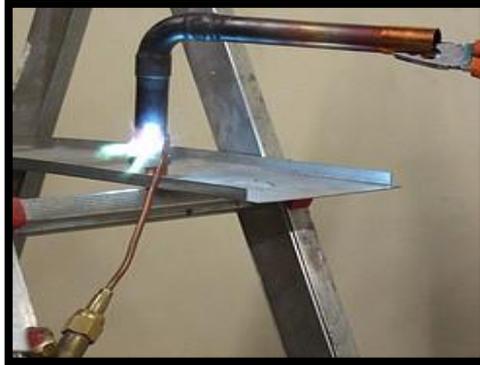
Soldadura a gas o Soldadura Autógena
